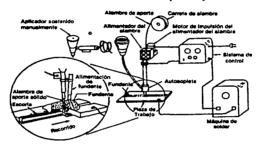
Parte de un sistema para soldadura de arco sumergido
